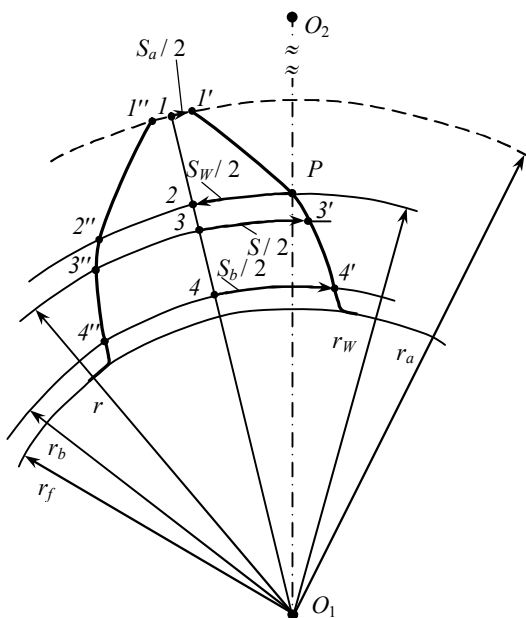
Построение бокового профиля зуба зубчатого колеса
